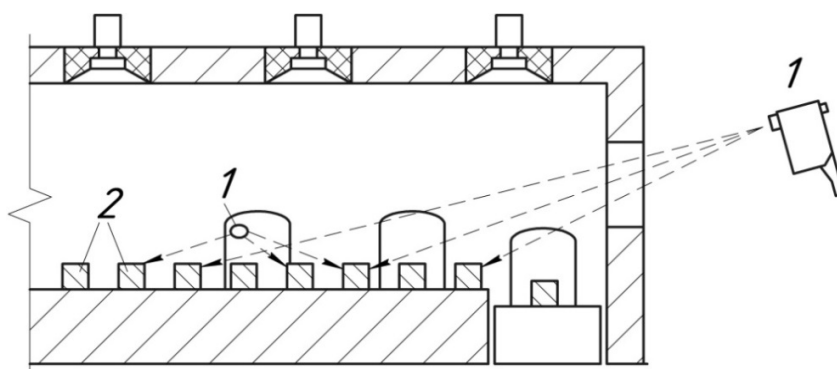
Схема измерений пирометром: 1 – радиационный или оптический пирометр; 2 – заготовки нагреваемого металла
